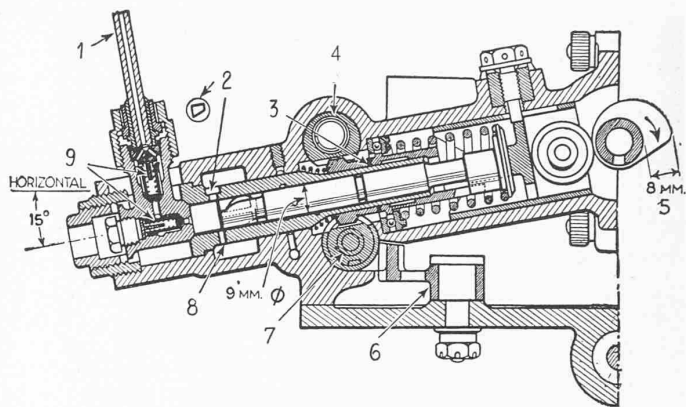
Benzineinspritzpumpe am Junkers-Flugmotor, Typ 211 A
